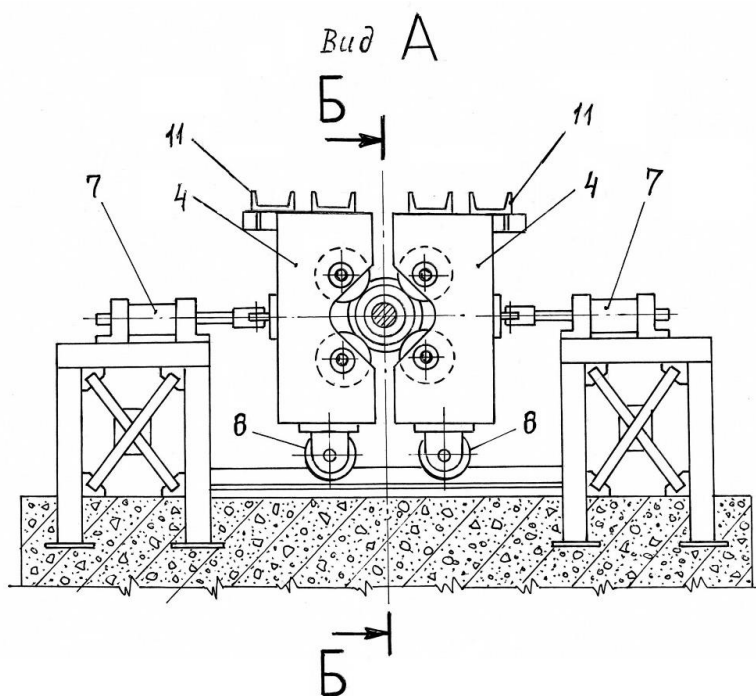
Обкатний пристрій (вид за стрілкою на рис. 3)
